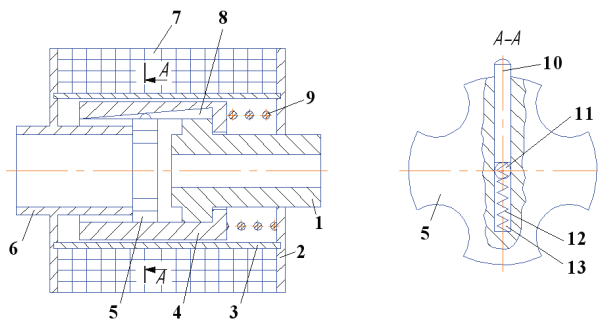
Демпфирующий дроссель: 1, 6 - штуцер подводящий и отводящий; 2 - диск; 3 - втулка; 4 - стакан; 5 - шайба подвижная; 7 - обмотка электромагнита; 8 - паз клиновидный; 9, 12 - пружина; 10 - толкатель; 11 - отверстие центральное; 13 - отверстие радиальное
